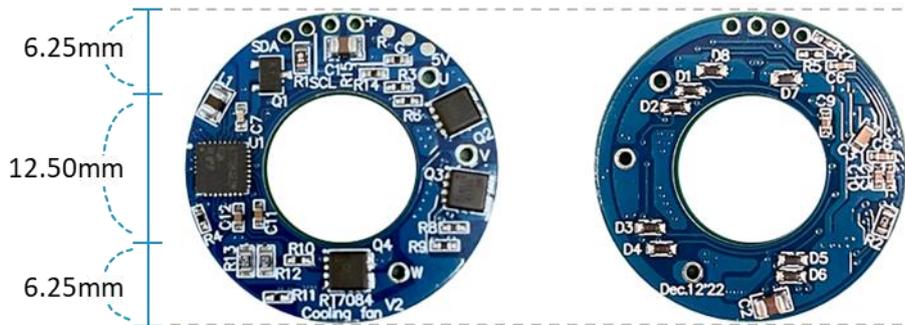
[RT7084](#) 在 4cm 伺服器風扇的 PCB Layout
